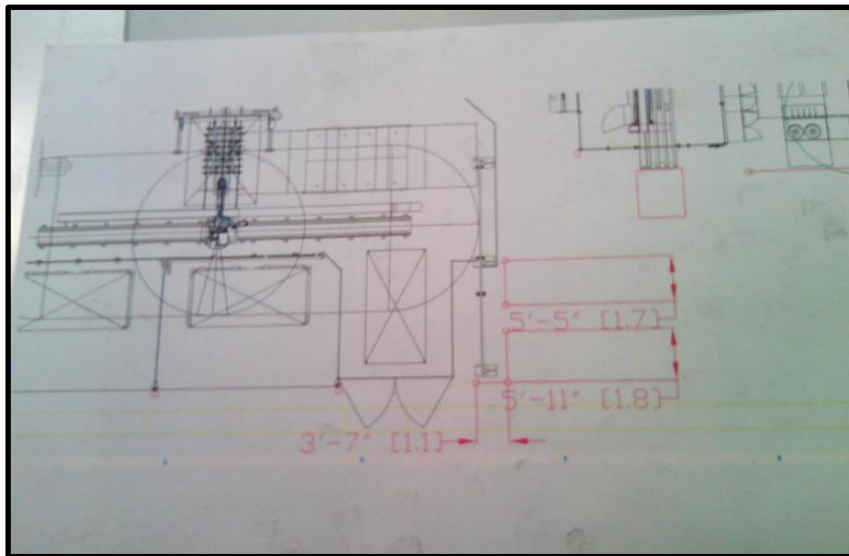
Plano de línea de soldadura láser (Soultrac).
